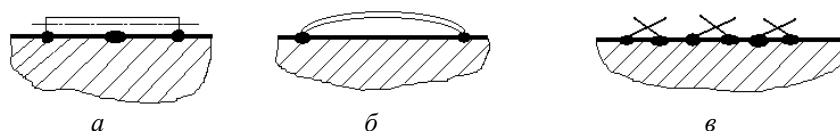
Варианты сварки проволоки с поверхностью: *а* – проволока размещена на поверхности; *б* – сварка обоих концов проволоки к поверхности; *в* – комбинация перекрещивающихся проволок
